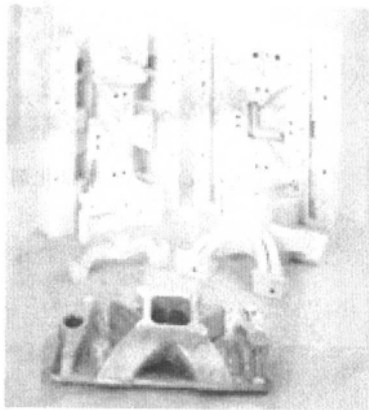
Z Cast Direct Metal Casting 工艺获得的铸件
